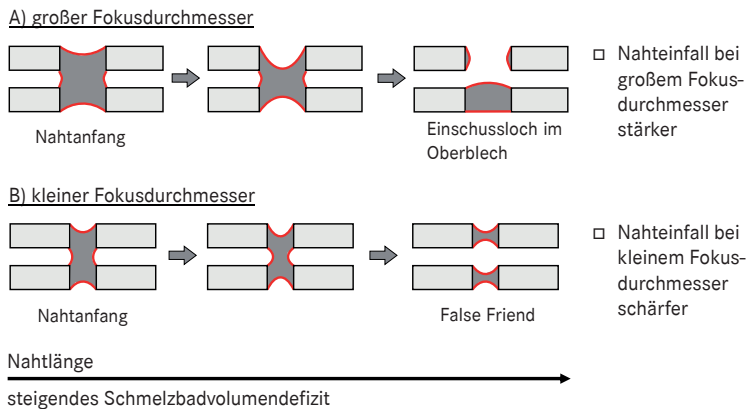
Querschnittsformen entlang einer Schweißnaht bei unterschiedlichen Fokusburchmessern beim Schweißen mit Spalt und dafür typische Fehler.
